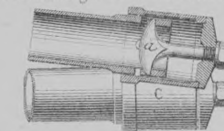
Assemblage des boîtes mères du bas sur le collecteur d'alimentation.
